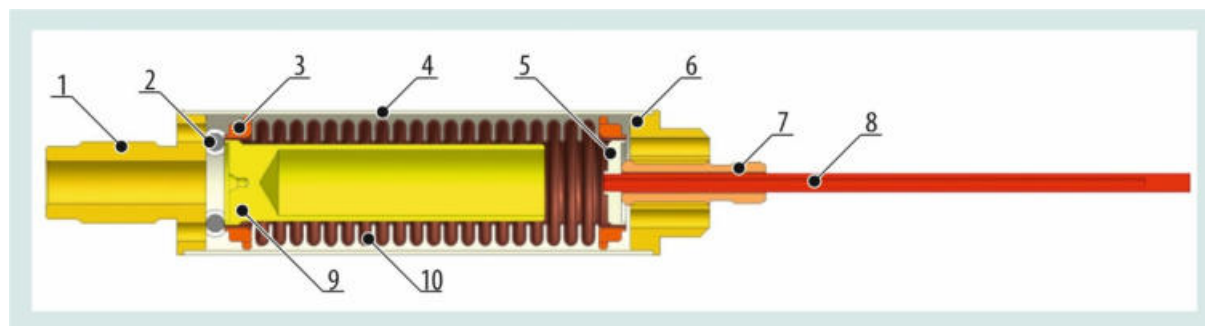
Схема блока нагрузки: 1 — наконечник; 2 — скоба; 3 — направляющие втулки; 4 — оболочка; 5 — кольцо; 6 — заглушка; 7 — регулировочный винт; 8 — канал; 9 — центральная втулка; 10 — сильфон
